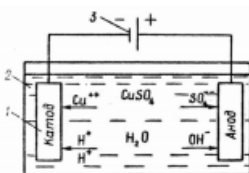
Схема установки для електролітичного осадження металу:
